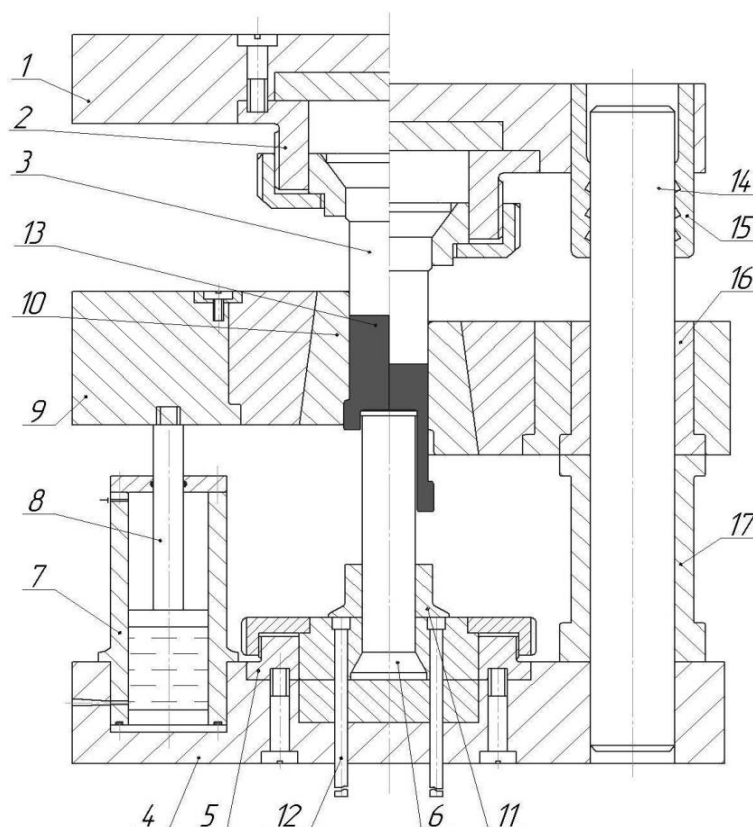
Схема штамп для реалізації способу комбінованого видавлювання порожнистих деталей з перемінною товщиною стінки
